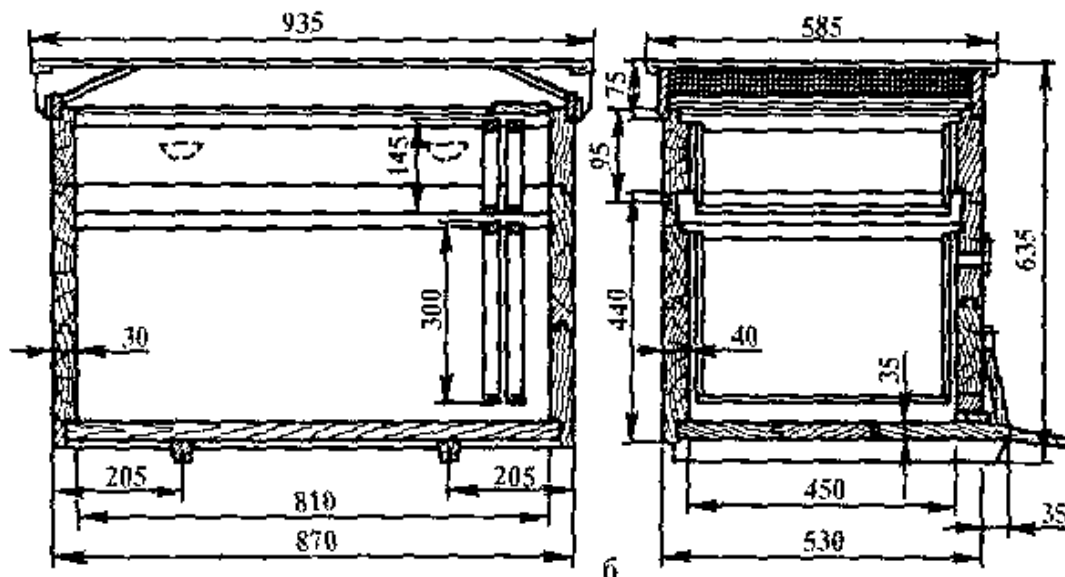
Улей – лежак двадцатирамочный с магазинной надставкою (продольный и поперечный разрез)
